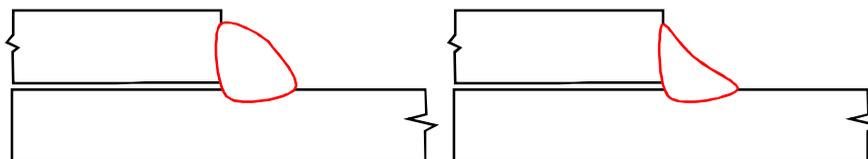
Perfiles de soldadura de filete inaceptables (izquierda) y aceptable (derecha)
